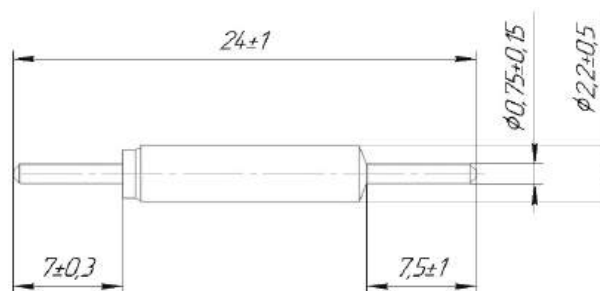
Габаритные размеры фильтров Ф26, типоразмер 2
